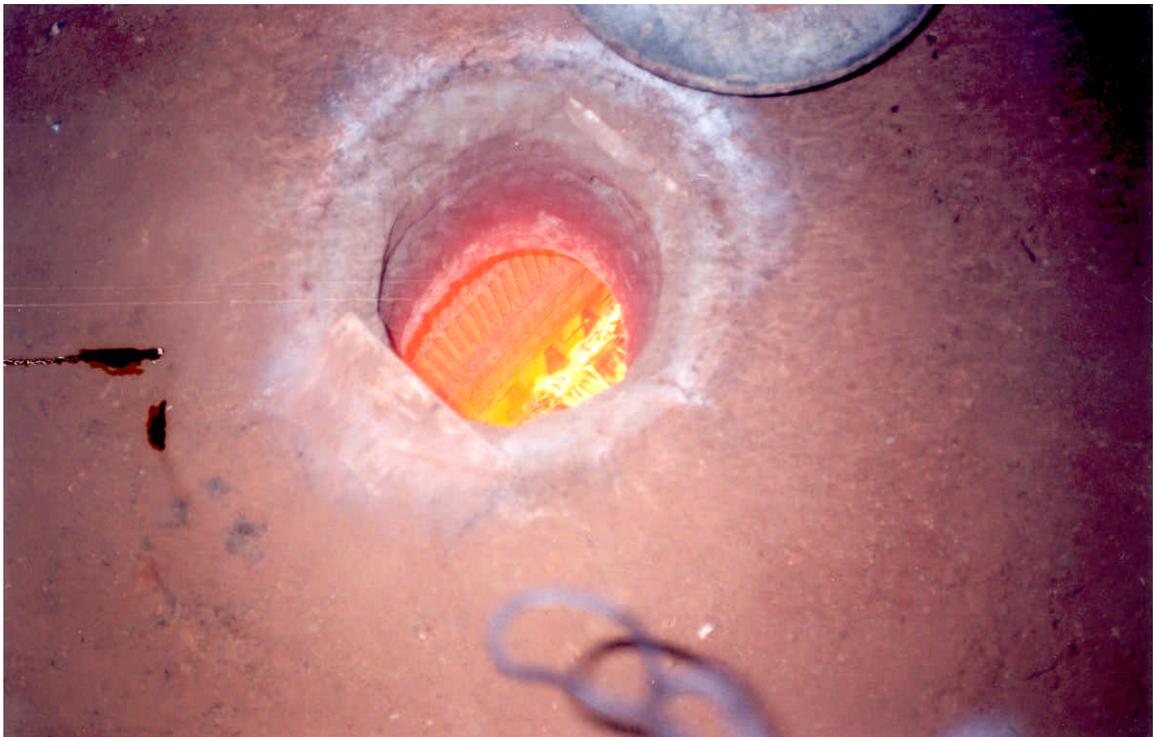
Queima em forno contínuo da Cerâmica Zampier (ponto IB-03)
